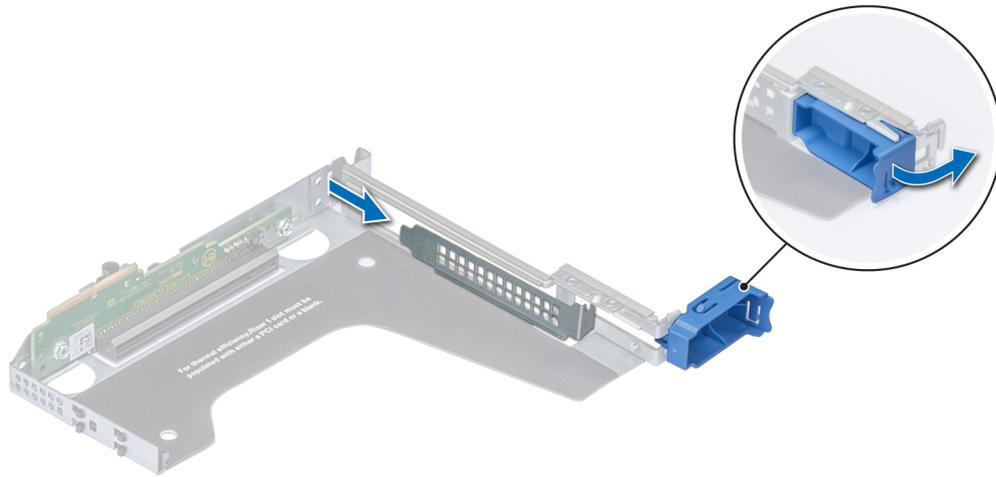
Retrait de la plaque de recouvrement pour la carte de montage 1
